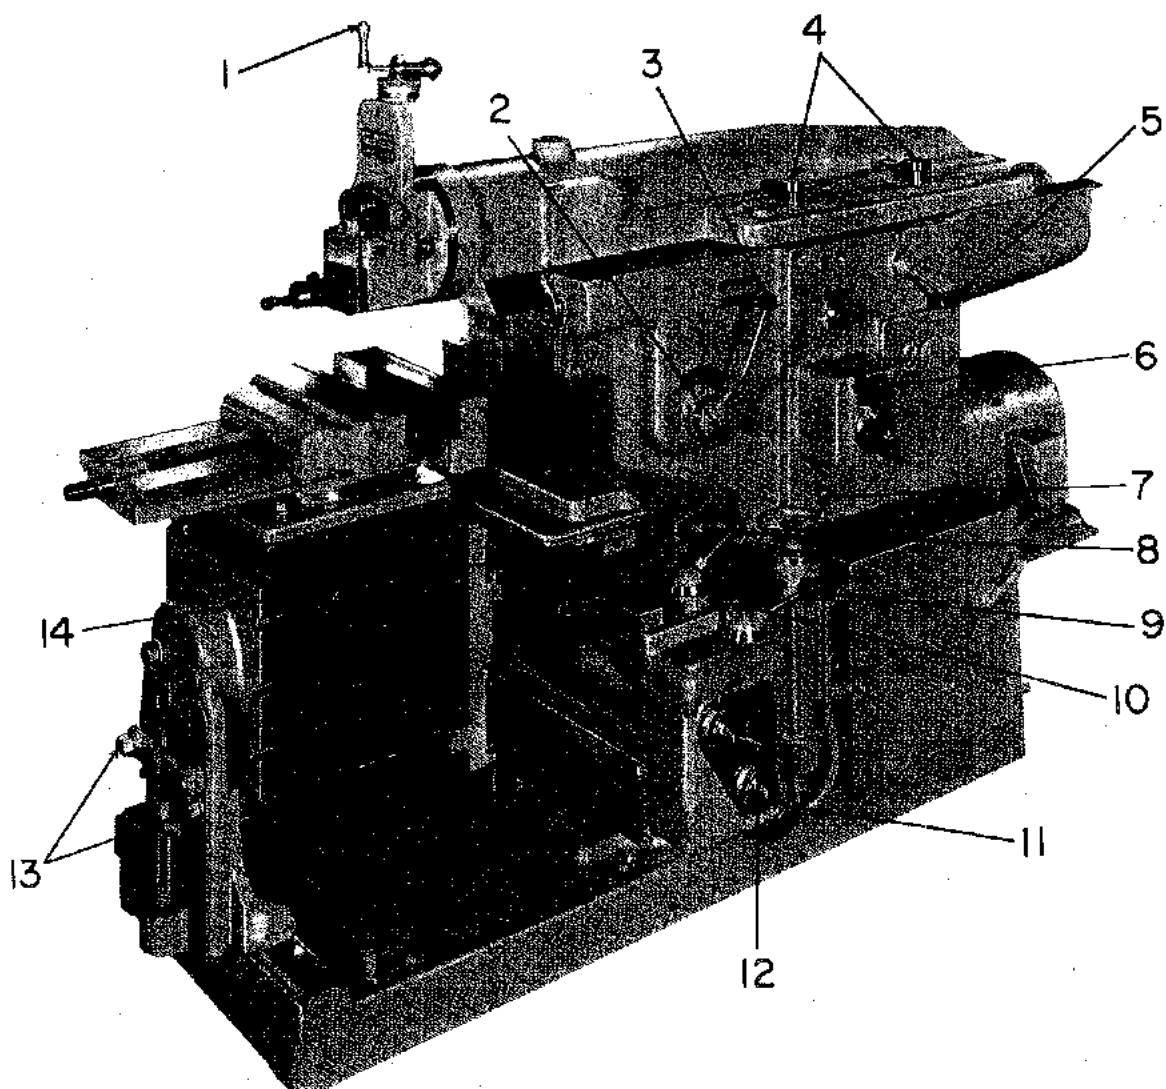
Palancas de mando y elementos de ajuste de una limadora hidráulica (Rockford Machine Tool Co.)
